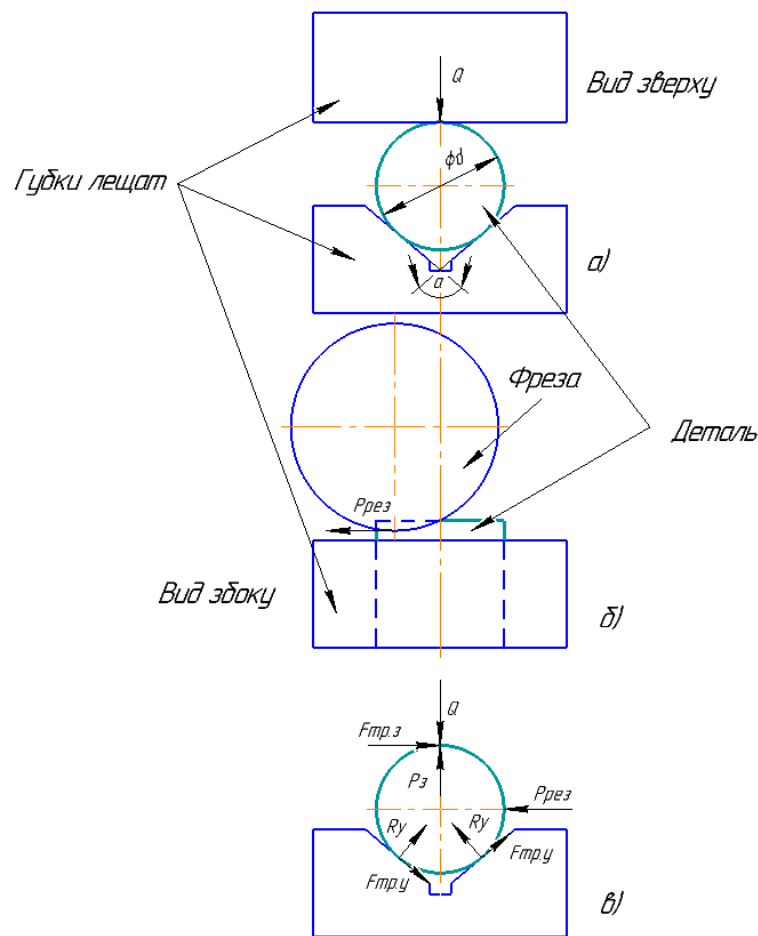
Схема яка показує сили, що виникають в процесі закріплення заготовки в призмі лещат: а) – вихідна схема для розрахунку; б) – вигляд збоку (фреза при обробці деталі); в) – активні сили при затиску заготовки.
